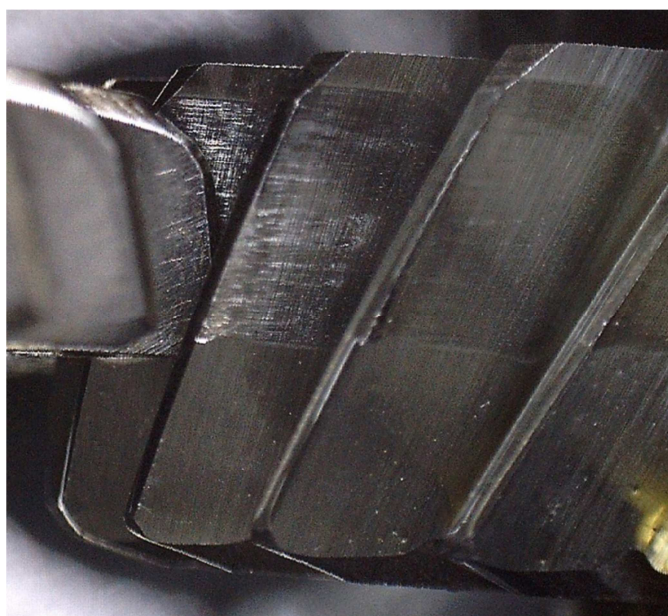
Ozubené soukolí HCR v testované převodovce
